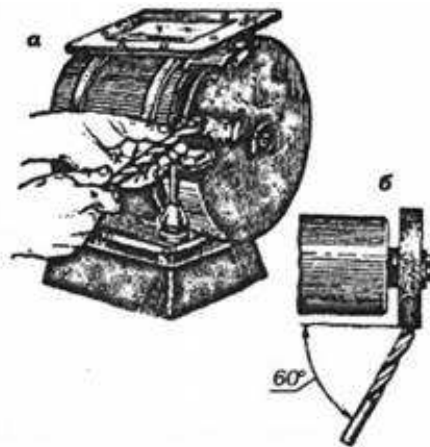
Заточка свердла: *а* – положення свердла в руках;
